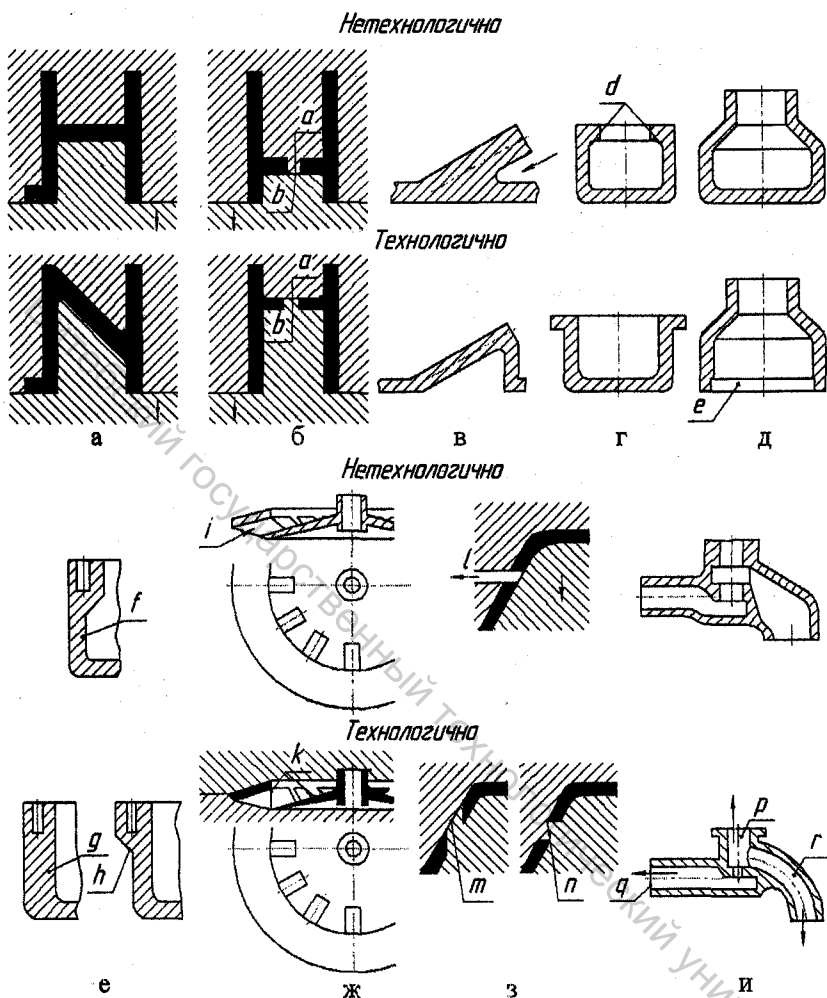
Примеры выбора технологичного варианта конструкции отливки
